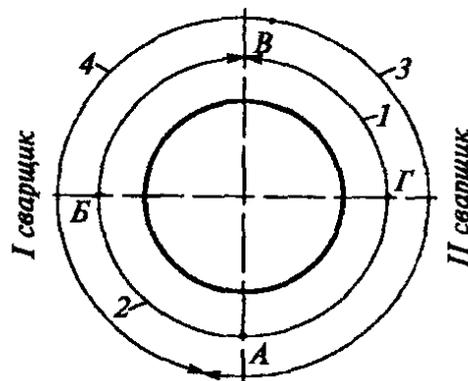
Порядок наложения слоев шва при сварке вертикального неповоротного стыка труб двумя сварщиками.
